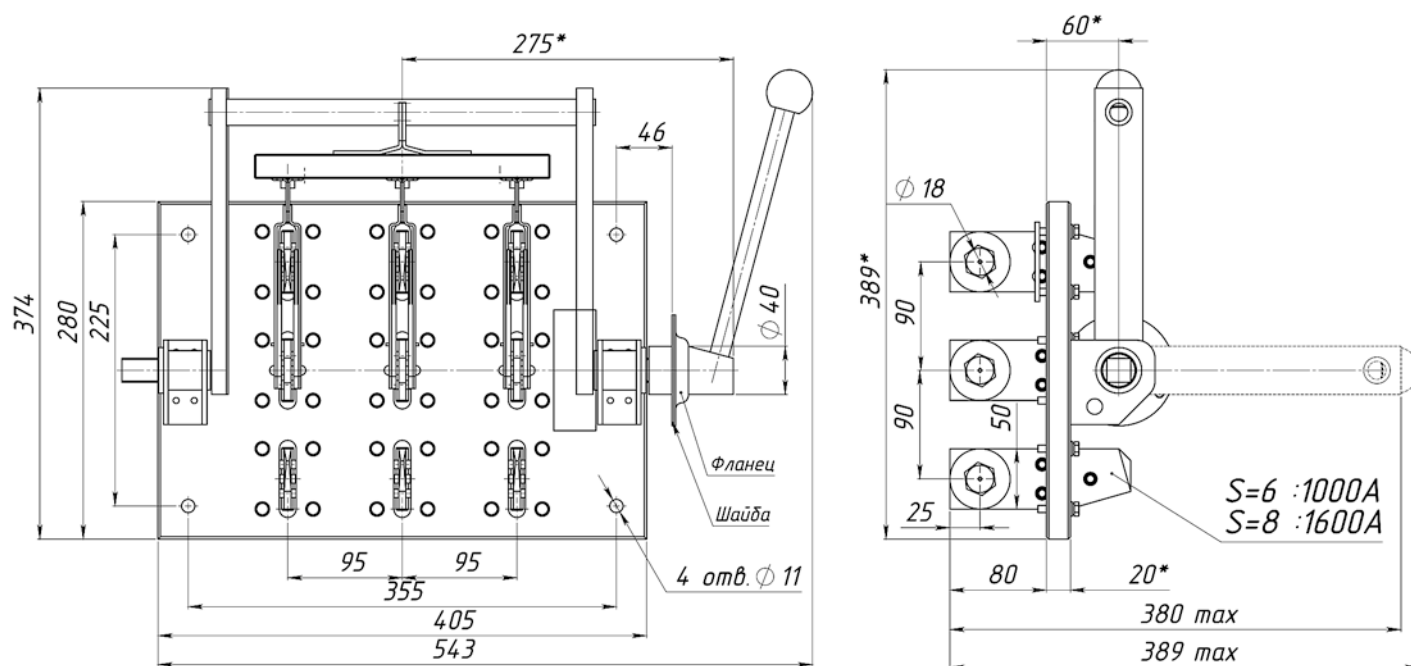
Разъединитель PE19-41(43)-72220-00 УХЛЗ на два направления с боковой рукояткой
